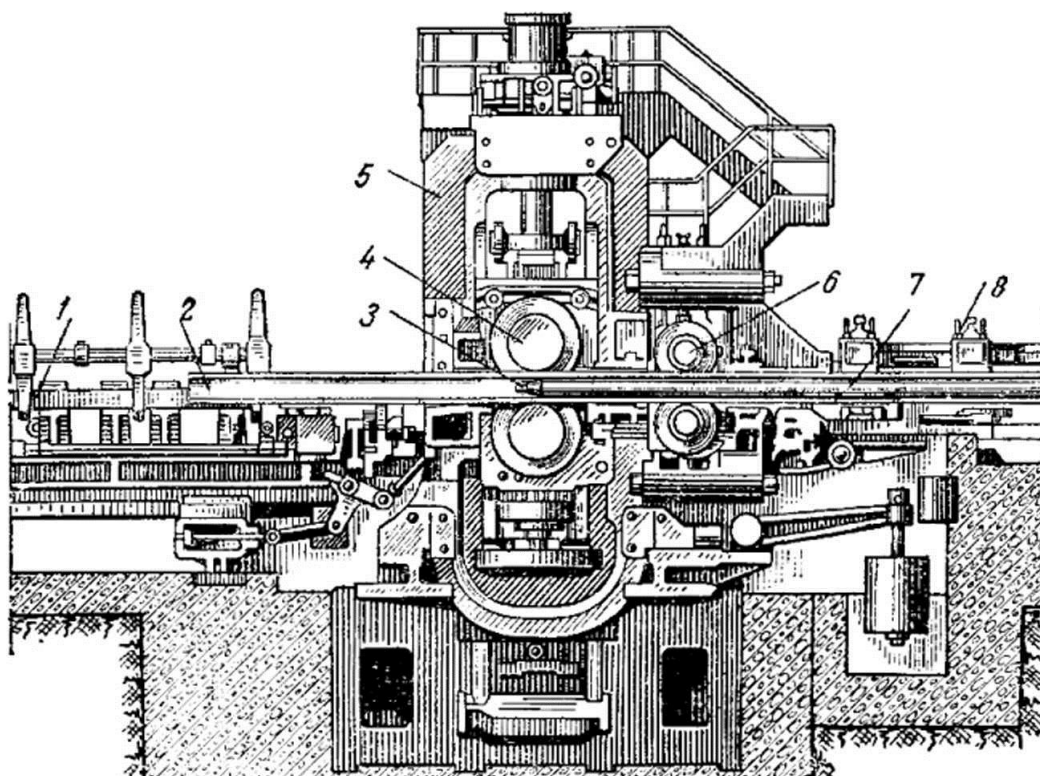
Робоча кліть автомат-стану: 1- передній стіл, 2 – гільза (трубна заготовка), 3- оправка, 4 – прокатні валки, 5 – станина, 6 – валки зворотної подачі, 7 – стрижень оправки, 8 – задній стіл.
